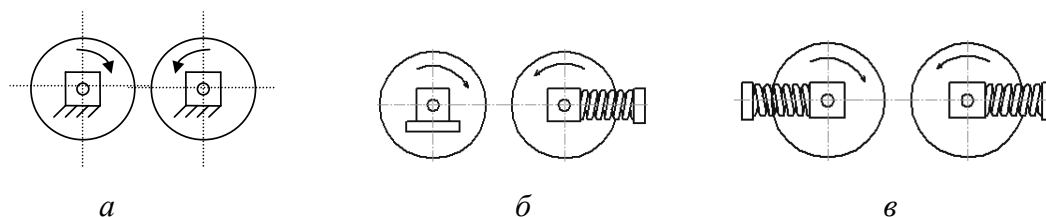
Конструктивне оформлення валкових дробарок:
